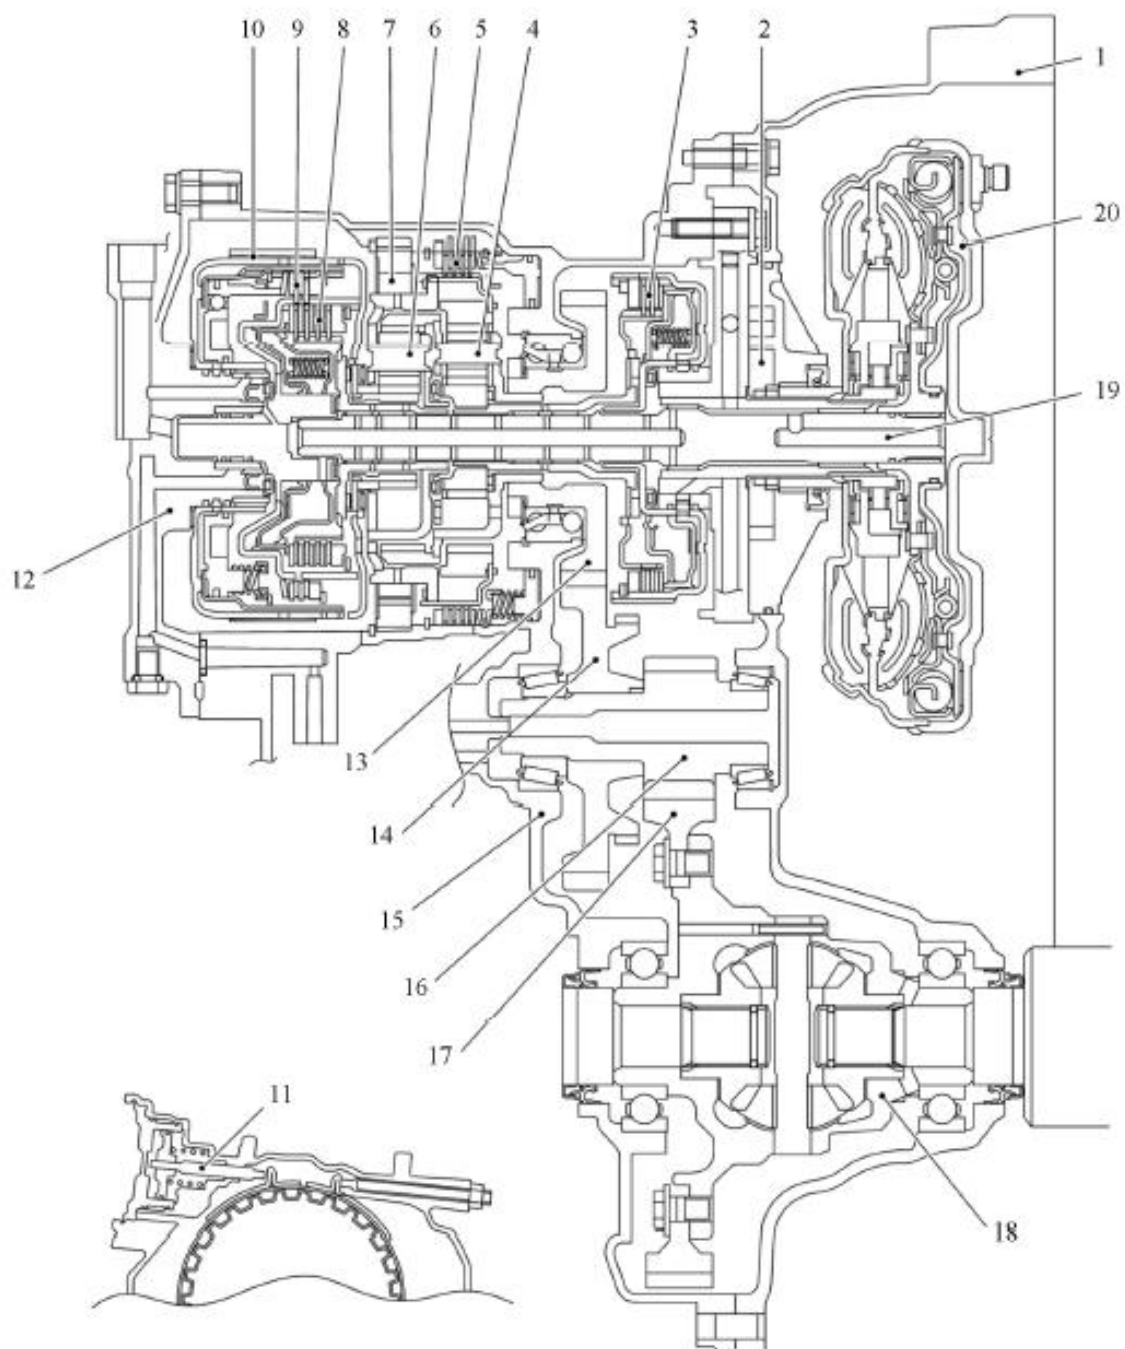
Устройство автоматической коробки передач автомобиля LADA GRANTA
